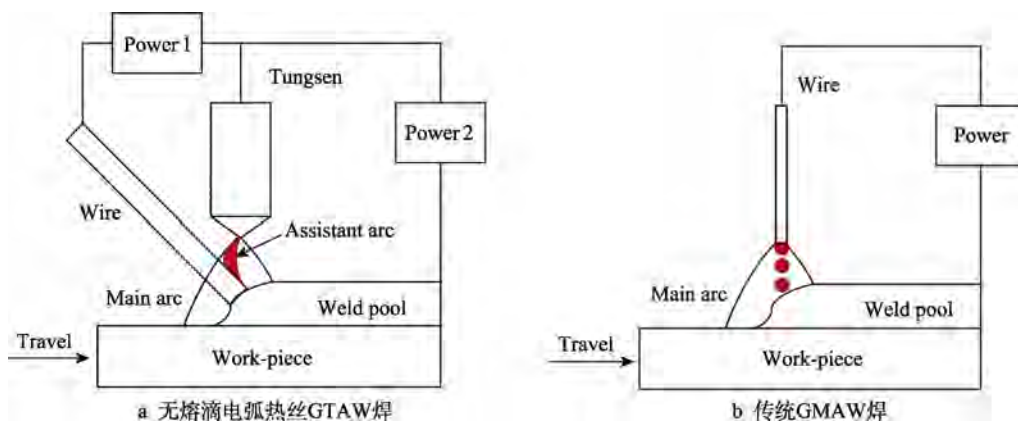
无熔滴电弧热丝 GTAW 和传统 GMAW 焊接原理示意图
